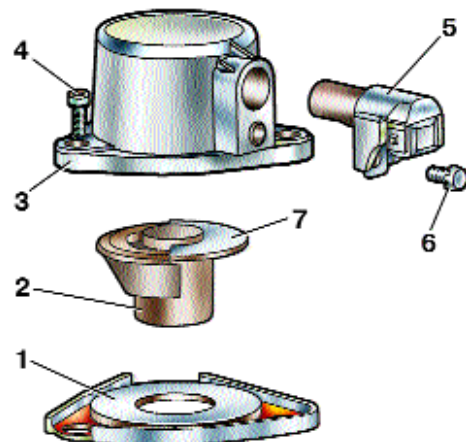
Устройство датчика порядкового номера цилиндра: 1 – установочная пластина; 2 – ротор; 3 – корпус; 4 – винт крепления корпуса; 5 – чувствительный элемент; 6 – винт крепления чувствительного элемента; 7 – реперный экран
